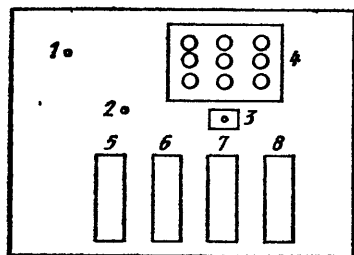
Схема рабочей зоны сборки амортизатора:
